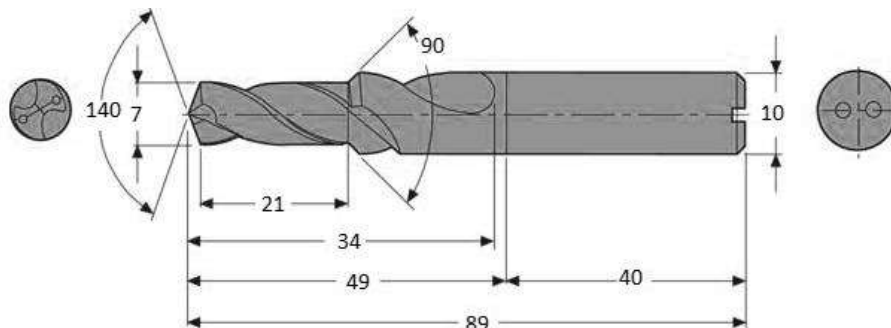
Сверло SD203A-C45-7.0-21-10R1
